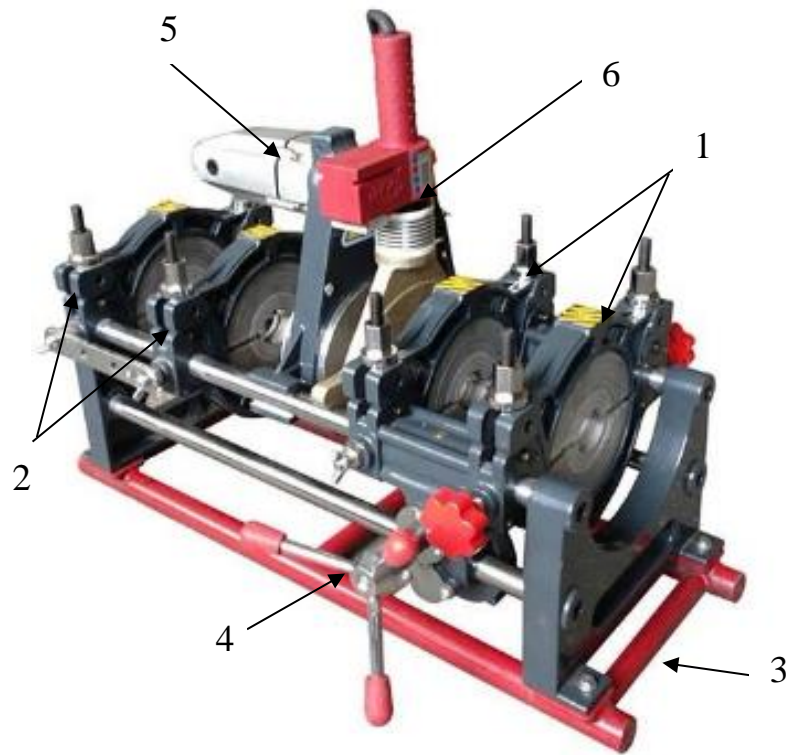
Состав оборудования с механическим приводом для стыковой сварки [41]
